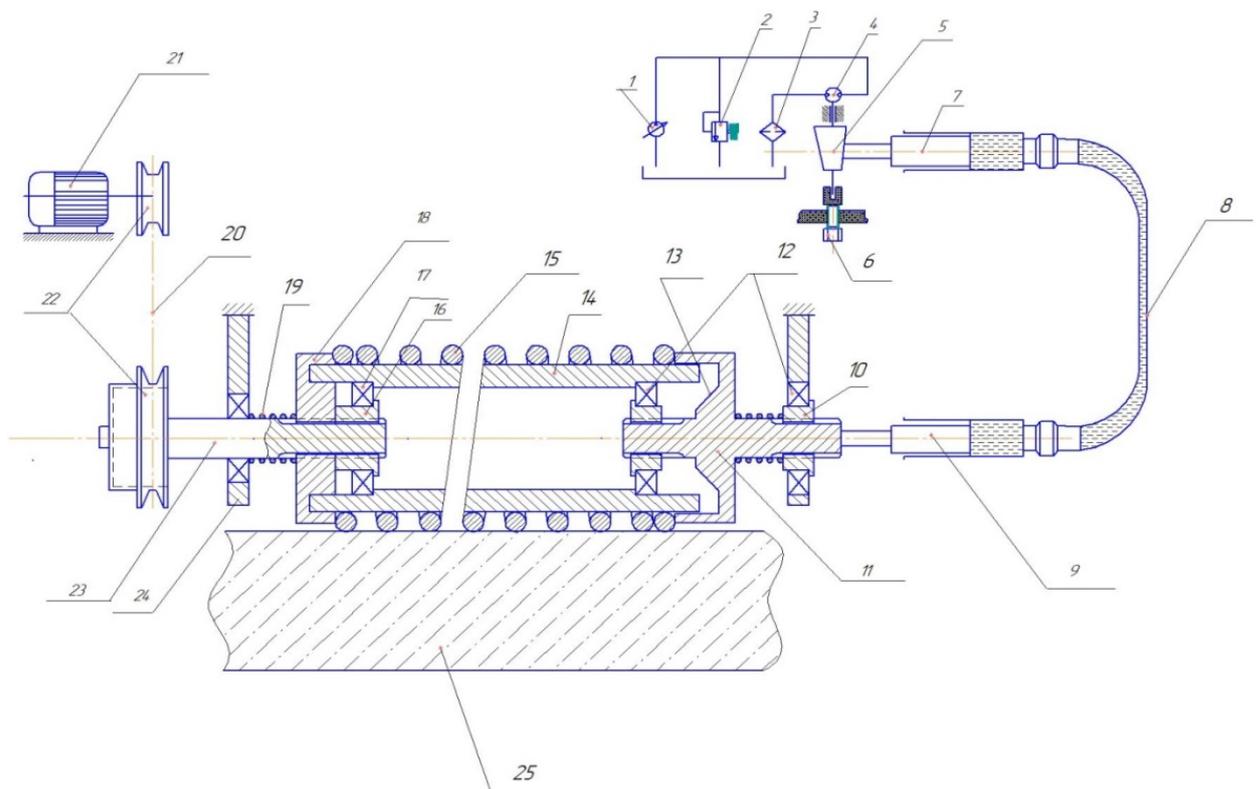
Валковый рабочий орган с поверхностью образованной пружиной [3]
